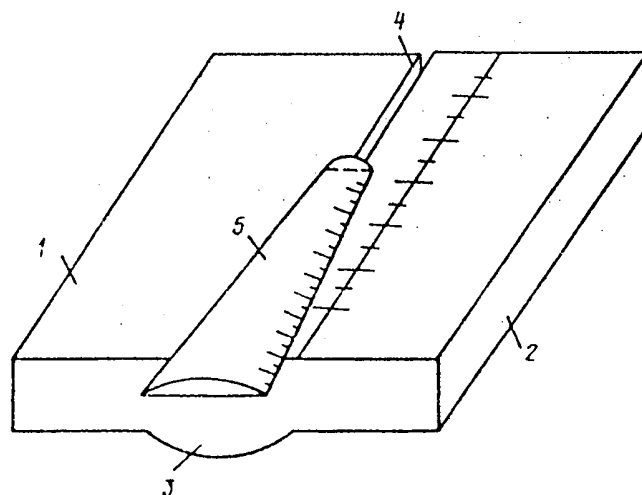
Контрольный образец для магнитного контроля качества двусторонних сварных швов
